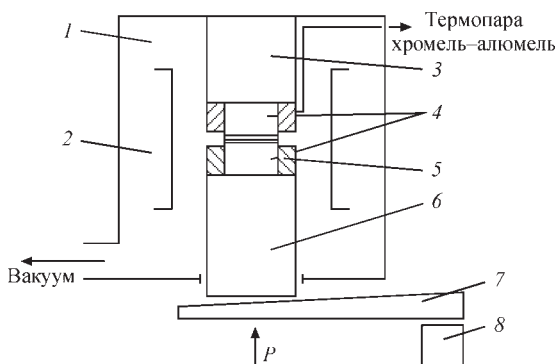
Схема установки для проведення дифузійного зварювання: 1 — вакуумна камера; 2 — молібденовий нагрівач; 3 — верхній шток; 4 — зразки з проміжним прошарком; 5 — оснащення; 6 — нижній шток; 7 — клин; 8 — прес
